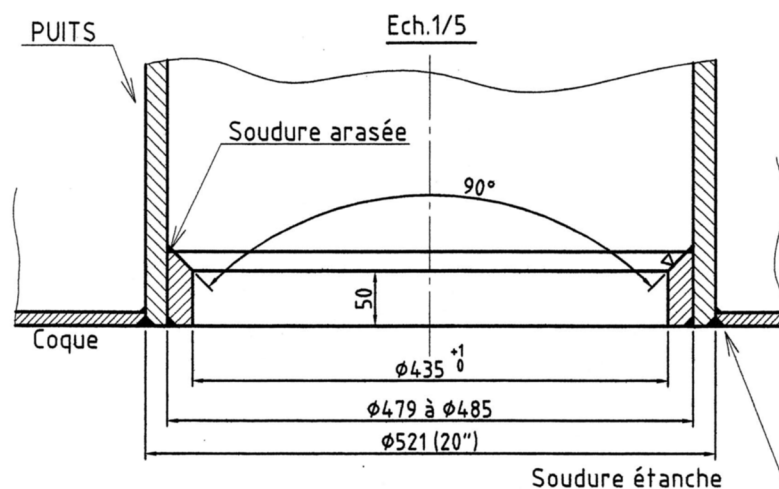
Plan de détail de l'appui au fond du puits 20"
